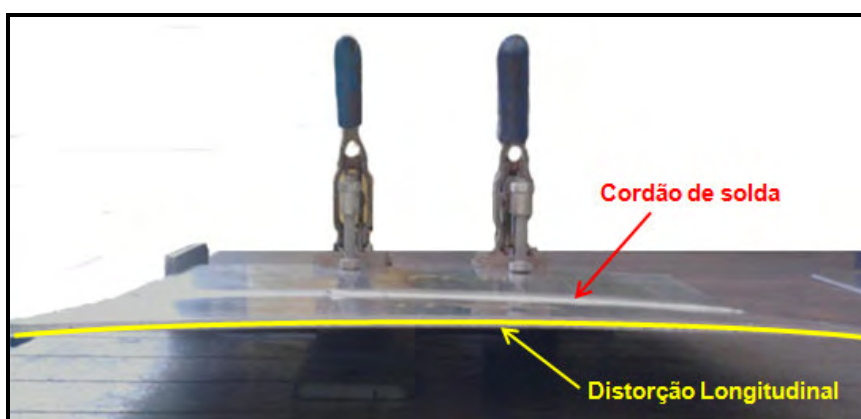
Distorção longitudinal “perfil parabólico com concavidade para baixo”.
